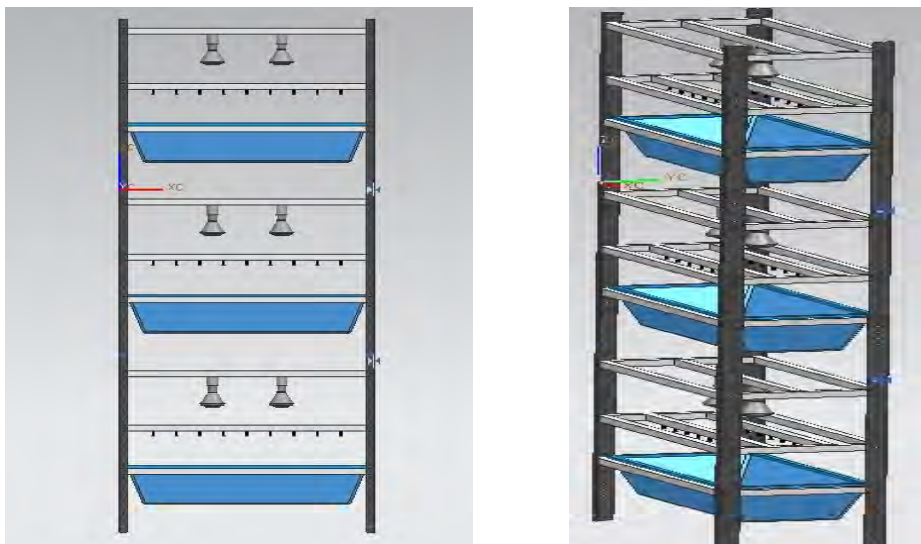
Estructura triple de módulo germinador de plántula.
